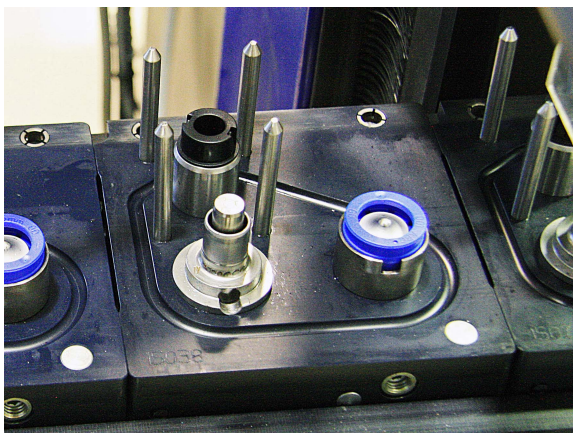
Bildet er fra en Mikronmaskin der en aktuator griper o-ringer fra en pallettfikstur for deretter å plassere den over et cone element
